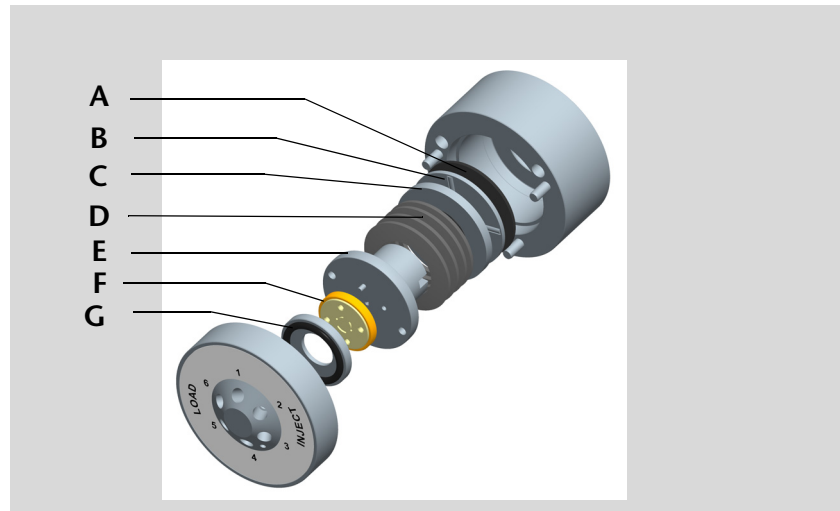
Explosionsdarstellung eines elektrischen Ventils
